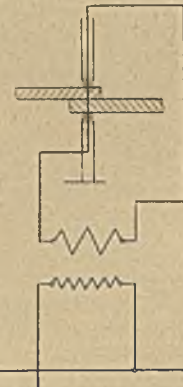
Widerstandsschweißung mittels transformierten Wechselstromes: Punktschweißung.
